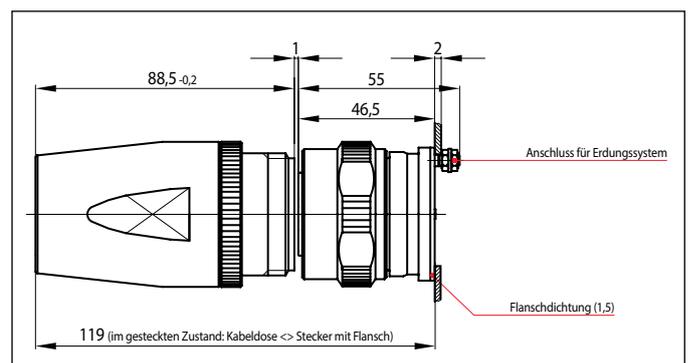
Einbaumaße und Maße im gesteckten Zustand für die Kombination Kabeldose und Stecker mit Flansch
